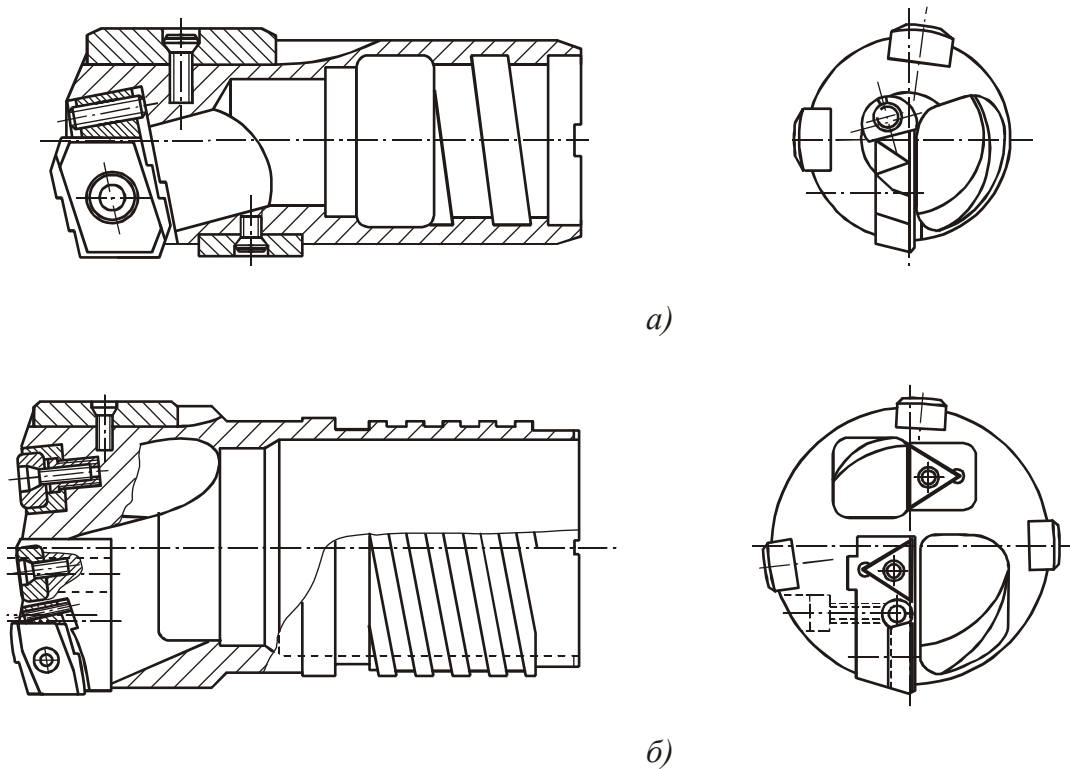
Сборные сверлильные головки БТА фирмы «Botek» (ФРГ):
